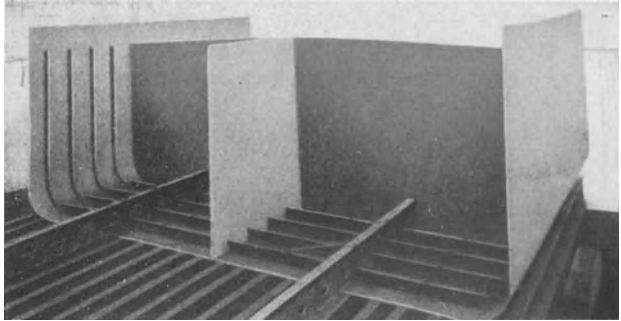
Teil eines ganz geschweißten Motortankboots.
